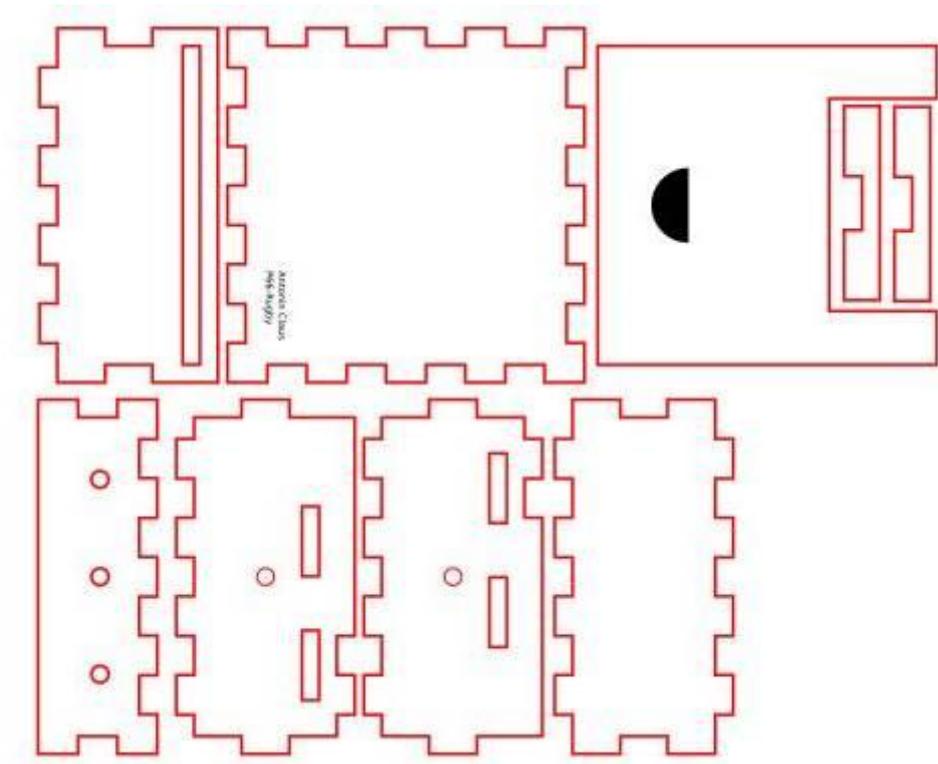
PLAN DE DECOUPE D'UN PLOT
